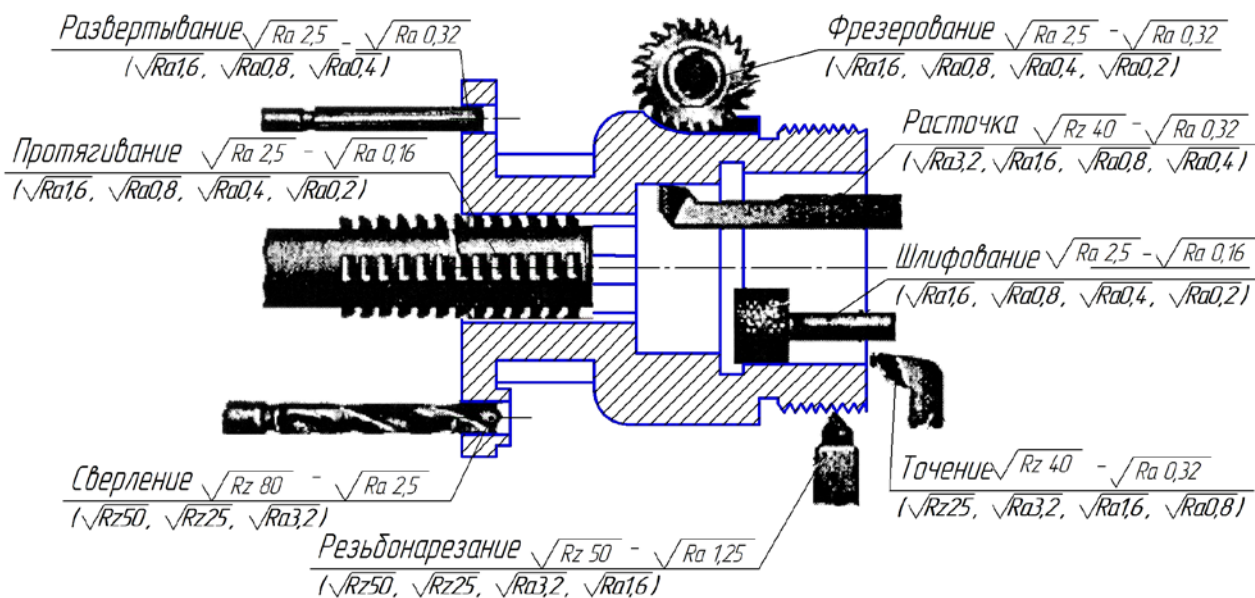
Виды обработки поверхности<sup>7</sup>
